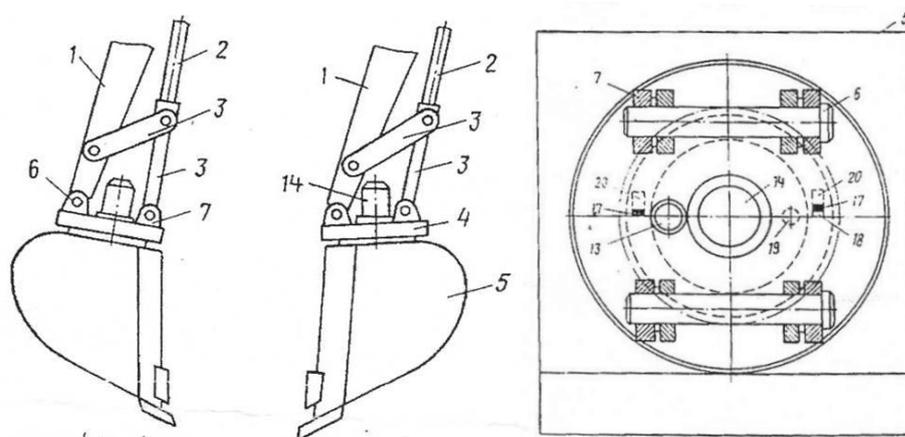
Предлагаемая конструкция рабочего оборудования одноковшового экскаватора
